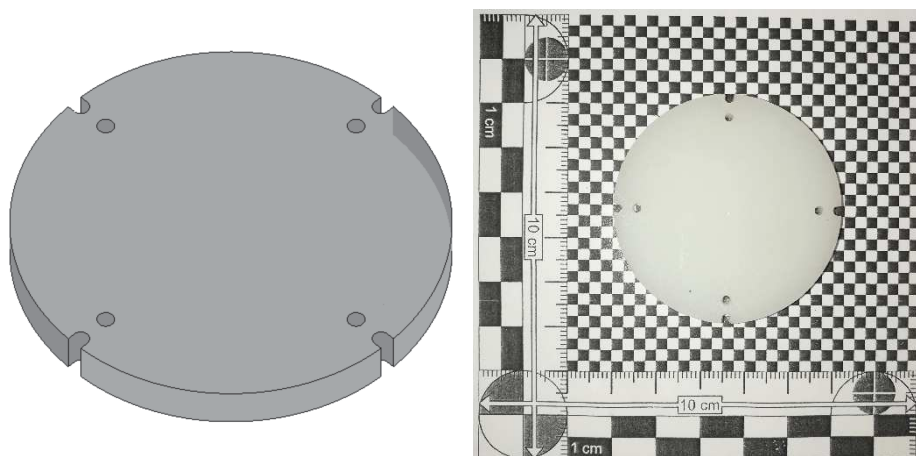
Base des masques : à gauche, modèle 3D ; à droite photographie.
